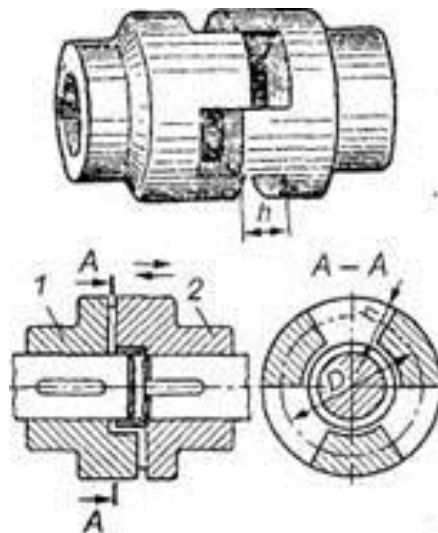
Конструкція кулачково-розширювальної муфти.
